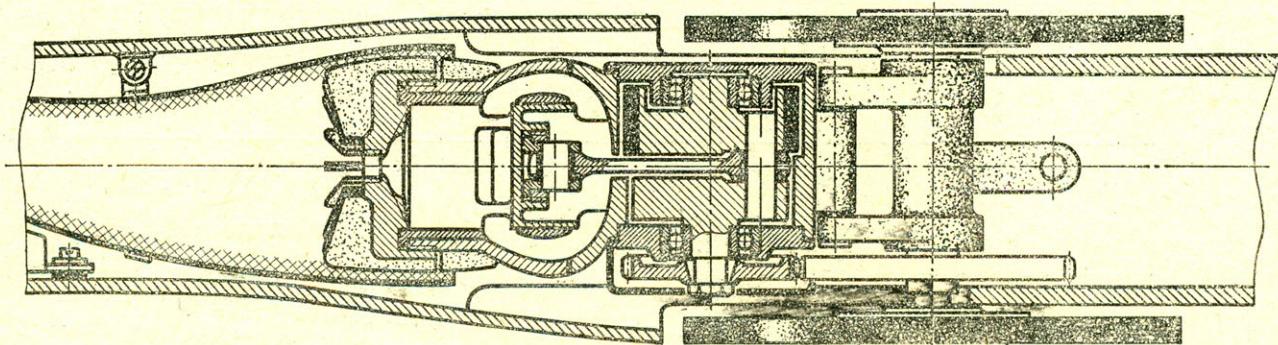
Мотоустановка с двухпорным коленчатым ва-
